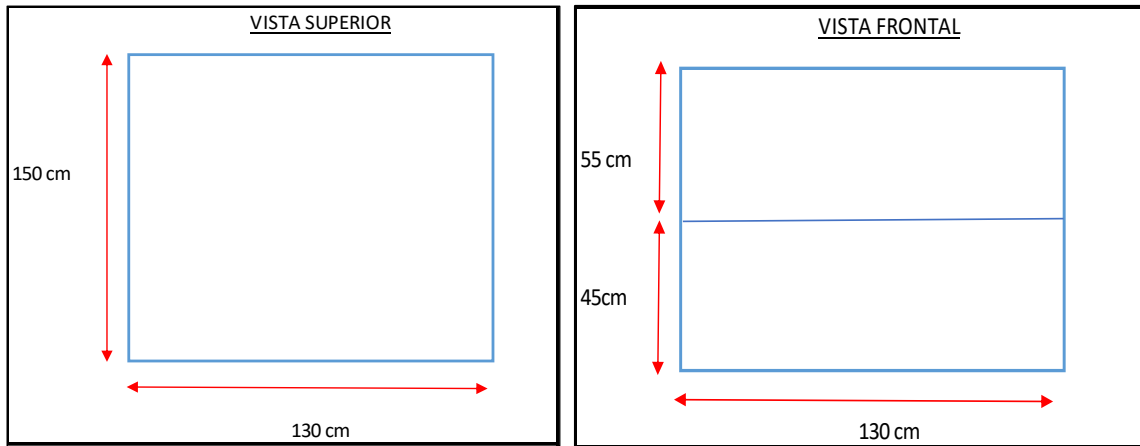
Dimensiones y distribución del horno de moldura antes de la propuesta
